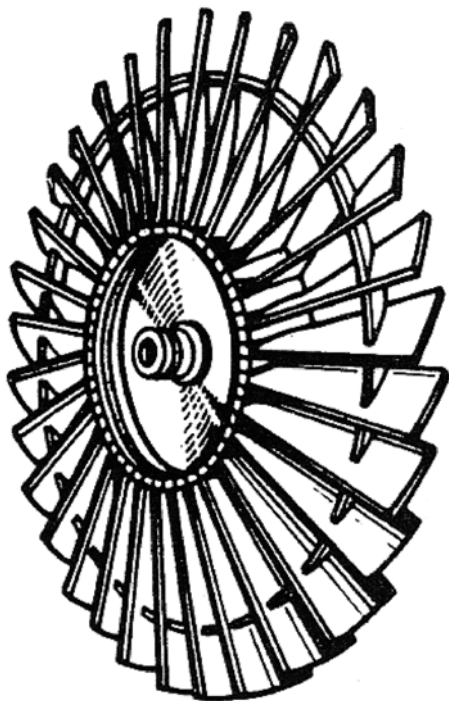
Рабочее колесо первой ступени ротора компрессора низкого давления
